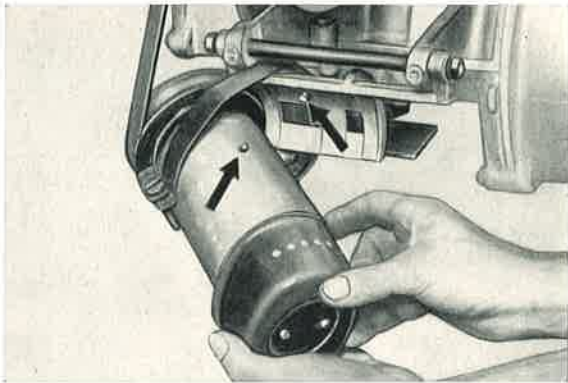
Beim Einbau der Lichtmaschine ist darauf zu achten, daß der Stift im Schwenkarm in das entsprechende Loch der Lichtmaschine eingeführt wird.
